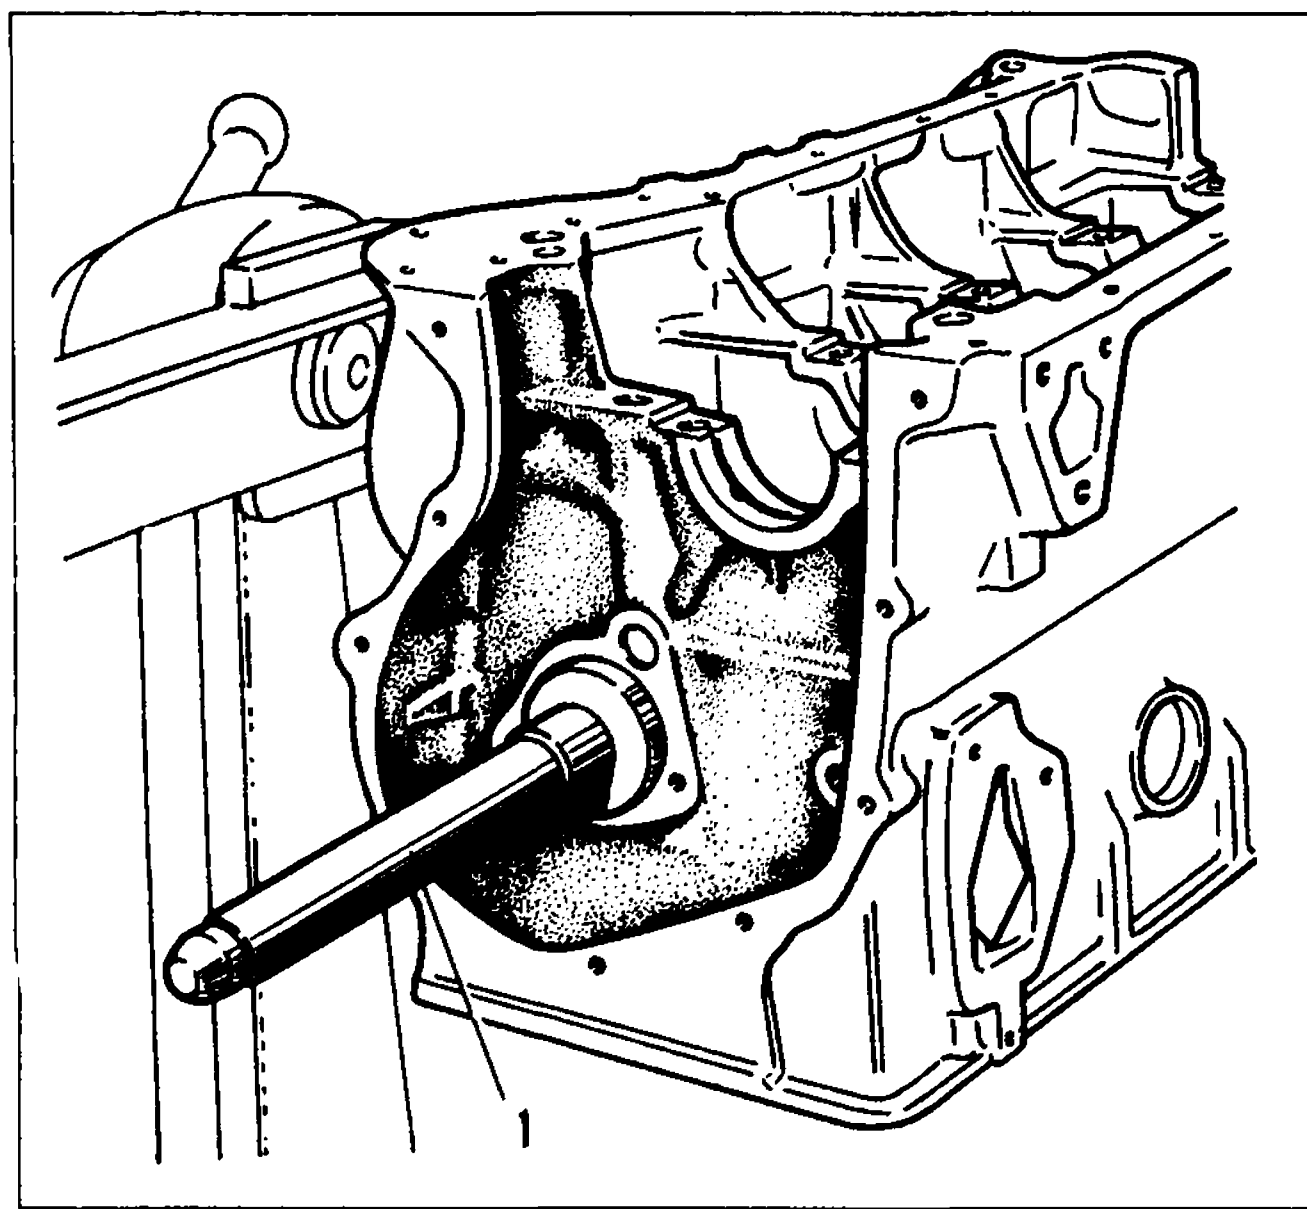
Снятие и установка втулок валика привода вспомогательных агрегатов:
